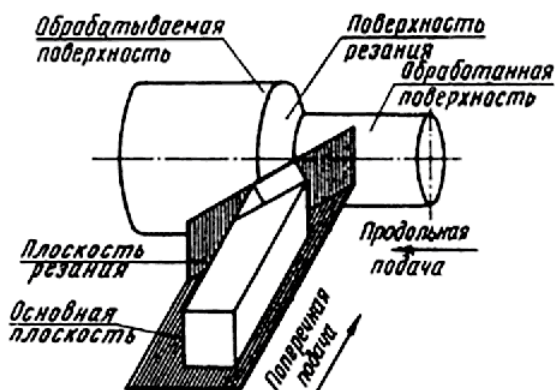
Основные поверхности заготовки и условные плоскости для изучения геометрии резца
